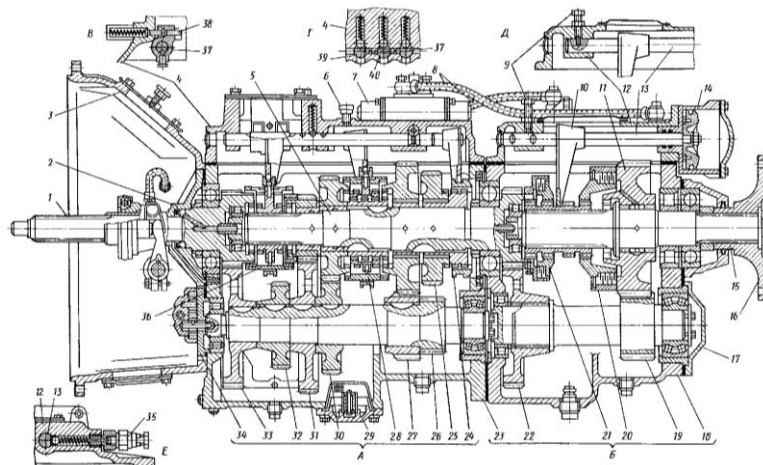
Будова Коробки передач автомобіля МАЗ-5551
